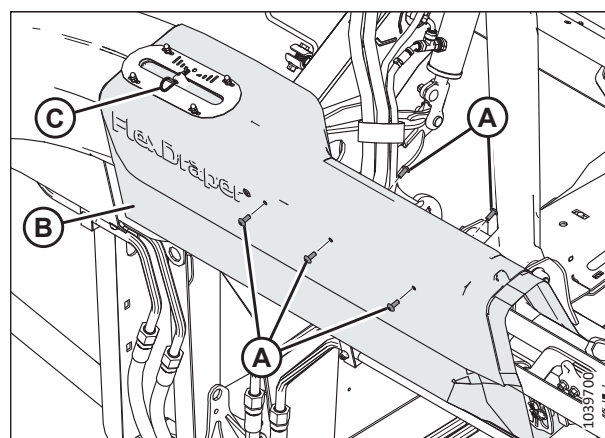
Levý kryt spojovacího ústrojí – zadní část adaptéru
